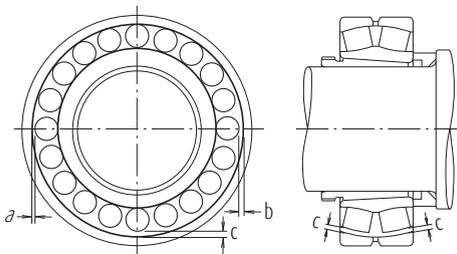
Měření vůle soudečkového ložiska
